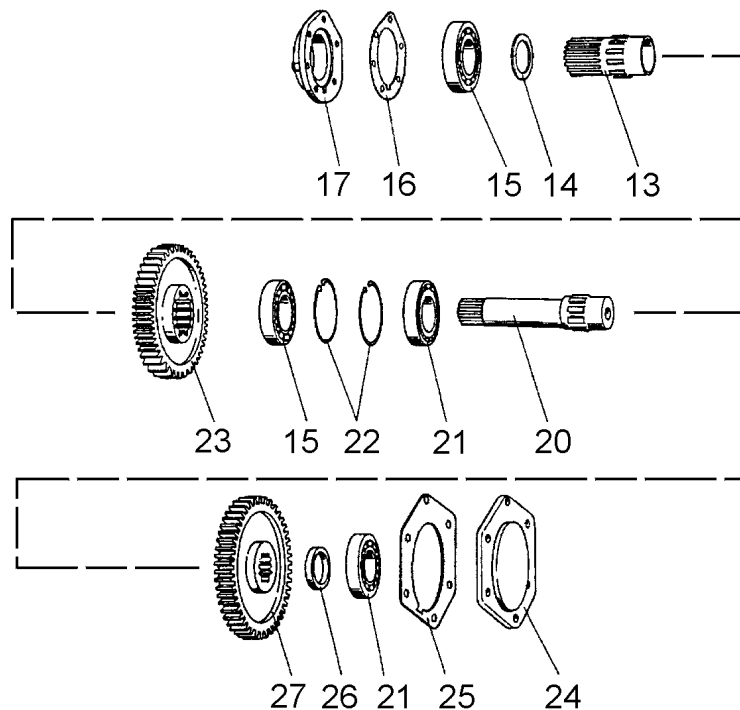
С.23. Вал заднего хода и вал медленного диапазона коробки передач
